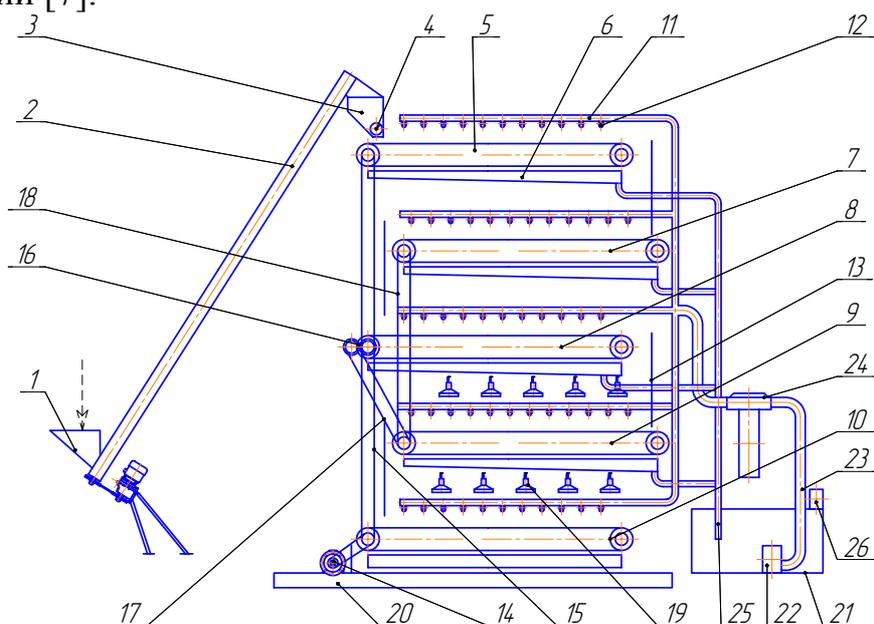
Конвейер для проращивания зерна 1, 3-бункер; 2, 4-шнек; 5, 7, 8, 9, 10-перфорированный транспортер; 6-емкость; 11-трубопровод; 12-форсунка; 13-щиток; 14-мотор-редуктор; 15, 17, 18-передача цепная; 16-блок шестерен; 19-лампы облучения; 20-рама; 21-емкость для воды; 22-насос; 23-трубопровод; 24-фильтр; 25-трубопровод сливной; 26-барботер
